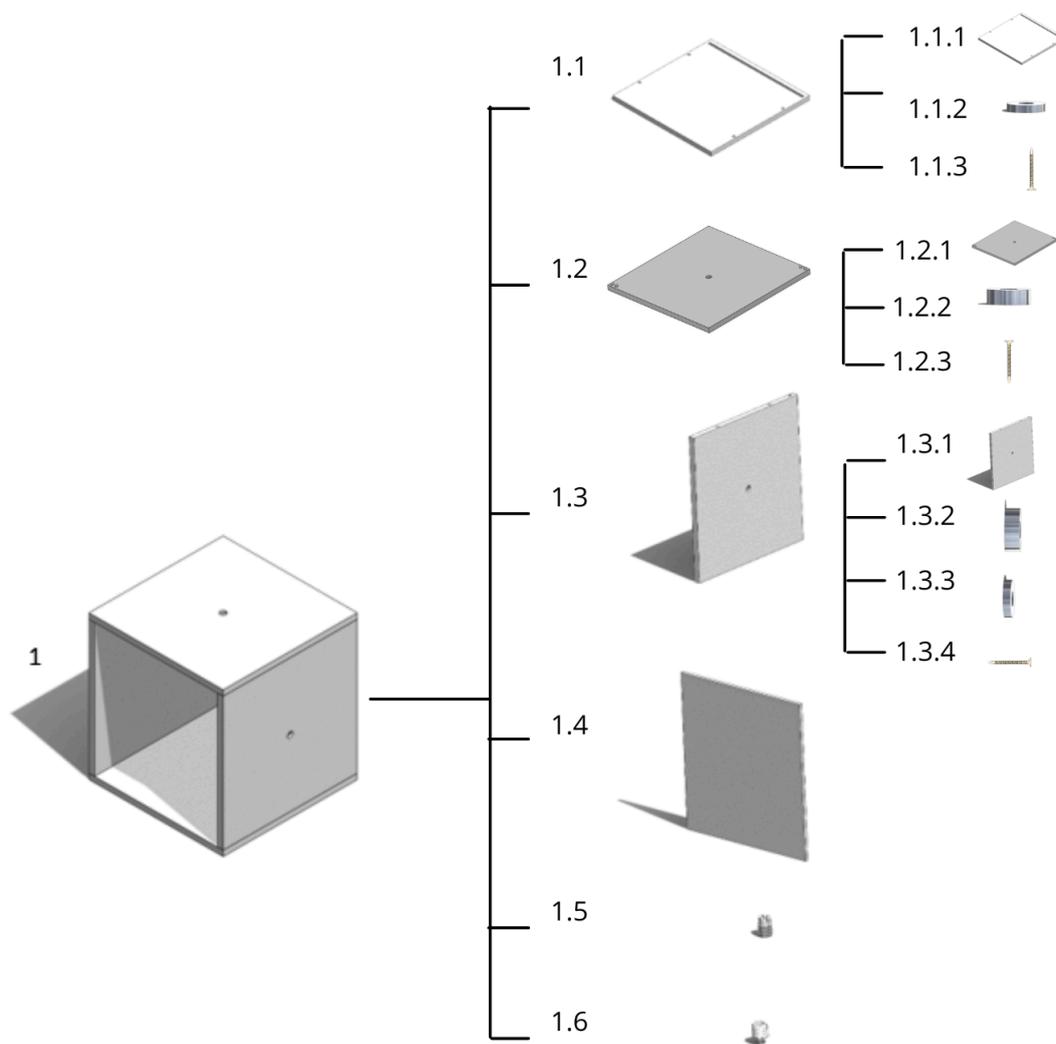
Esquema desmontaje del módulo del cubo sin puerta
